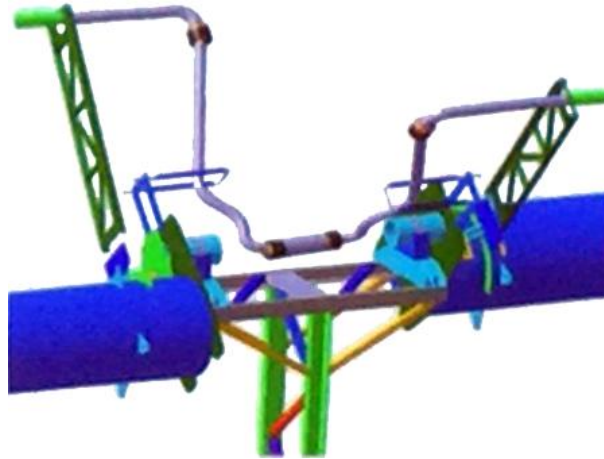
Detalles de Unión fija y móvil con rótulas: 3 rótulas (fija-móvil-dilatación)
